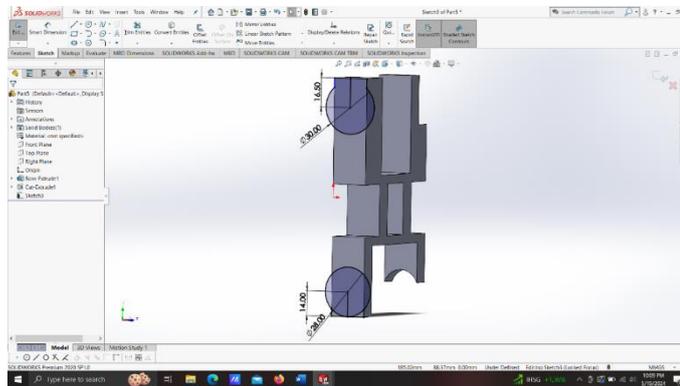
Extruded Cut Pada Sisi Samping Kanan
